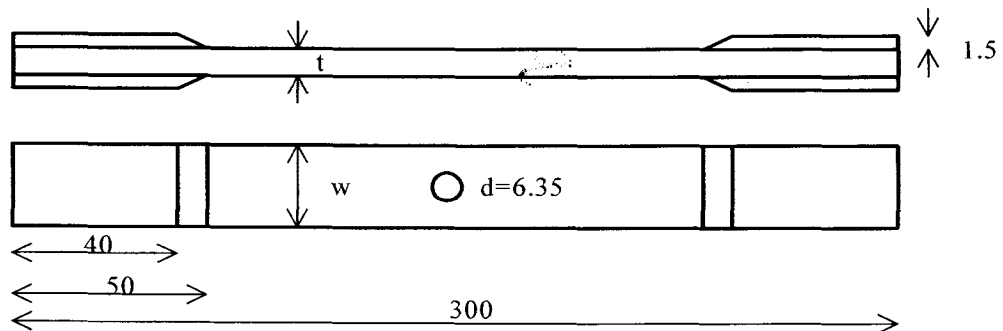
Open hole 인장시험의 시편 형상.
